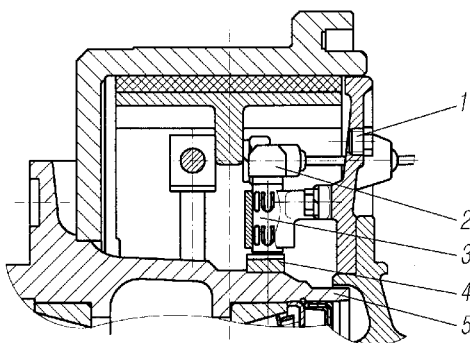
Механизм тормозной колесный: 1- пробка; 2- датчик индуктивный; 3- втулка зажимная; 4- кольцо импульсное зубчатое; 5- ступица колеса
